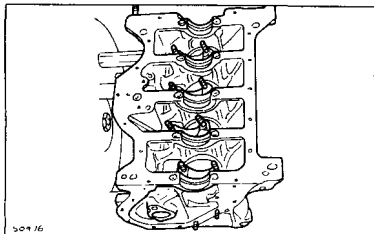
Вставьте вкладыши коренных подшипников в блок цилиндров
